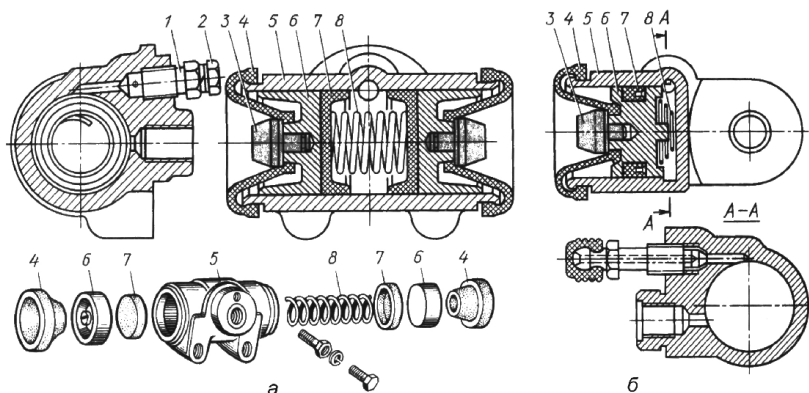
Колесные тормозные цилиндры гидропривода тормозных механизмов:
